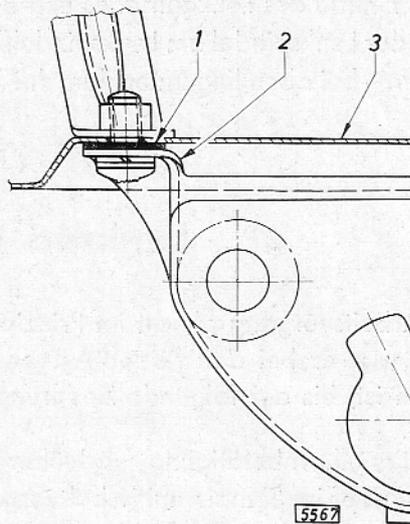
Linke Seite der Lenkstützrohrbefestigung
